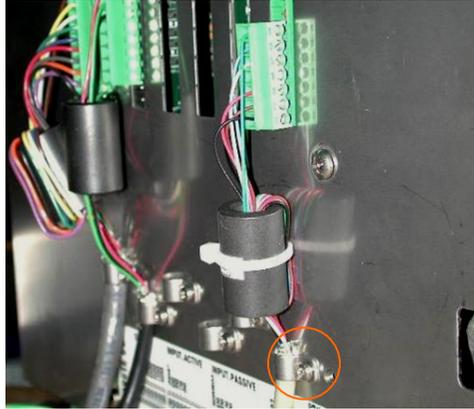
Terminazione del morsetto del cavo, armadietto montaggio a pannello
